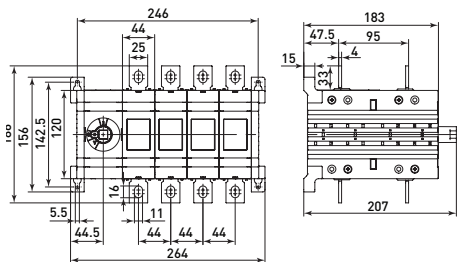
Габаритные и установочные размеры реверсивных рубильников 315-400А 4Р
